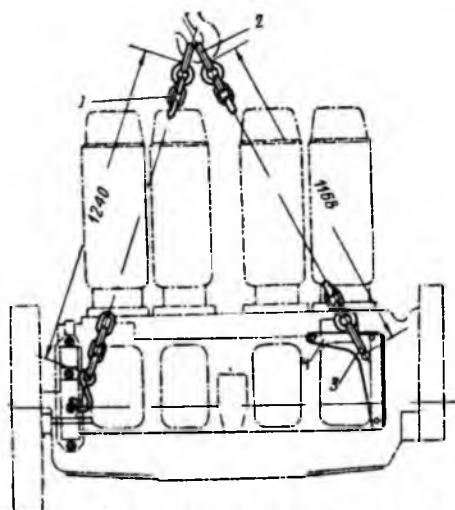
Цепь-схватка для двигателей ЧТЗ-С-60:
